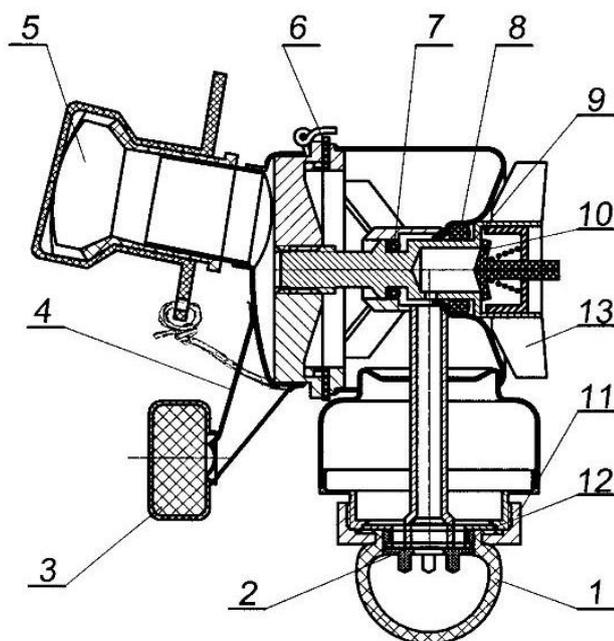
Часть лицевая (с мундштучным приспособлением)
